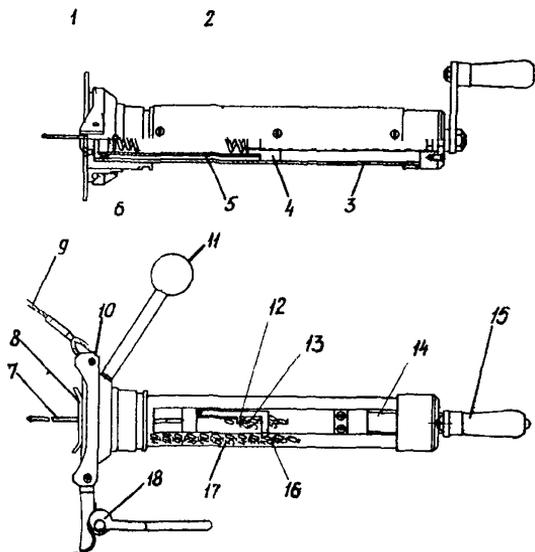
Общий вид прибора для определения степени загибания древесины опор:
